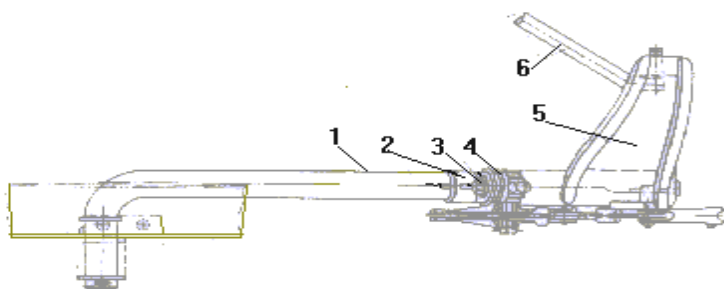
Тягова штанга з механізмом похилу косарки КСП-2,1 А:
